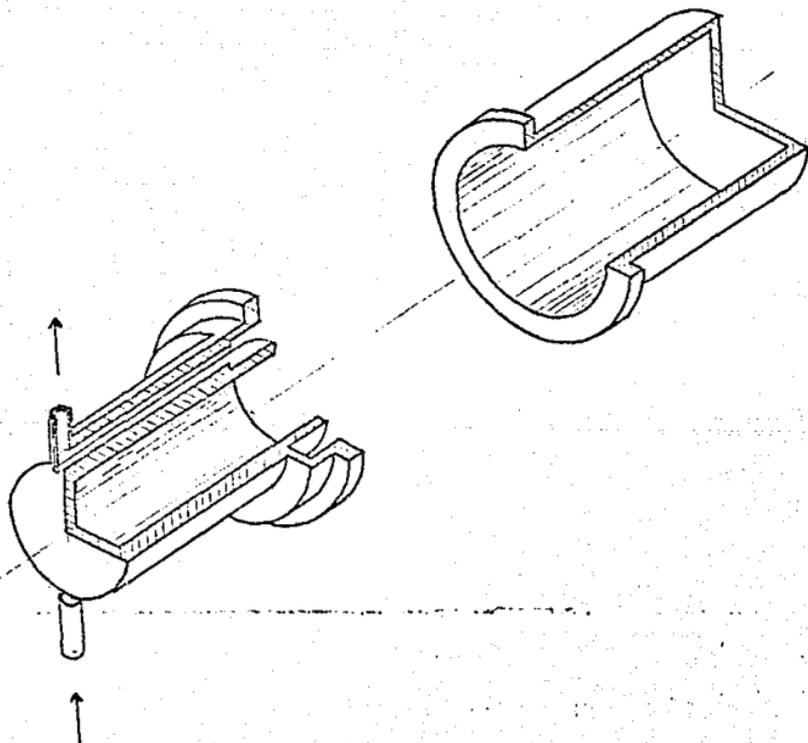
Sección transversal de la parte superior de la bomba vista de abajo.
